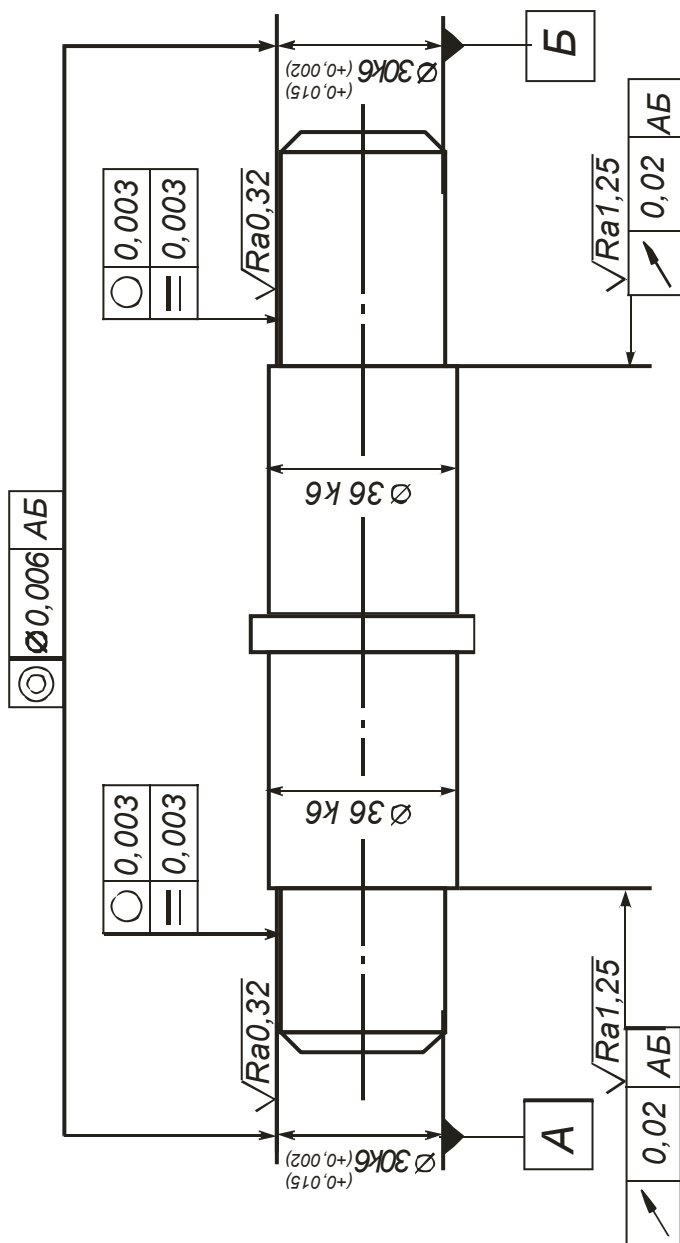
Пример обозначения требований к точности поверхностей вала, сопрягаемых с внутренними кольцами подшипников качения
